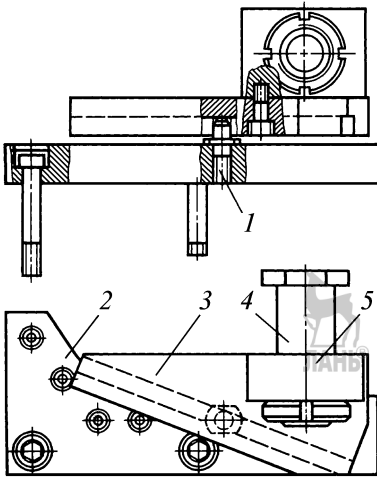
Приспособление для обработки конусов с большим углом уклона:
